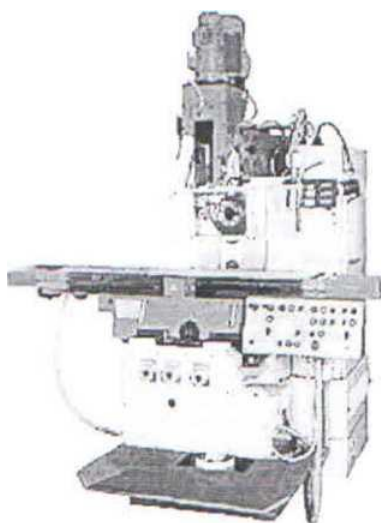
Широкоуниверсальный консольно - фрезерный станок Орша-ф32ш-11
